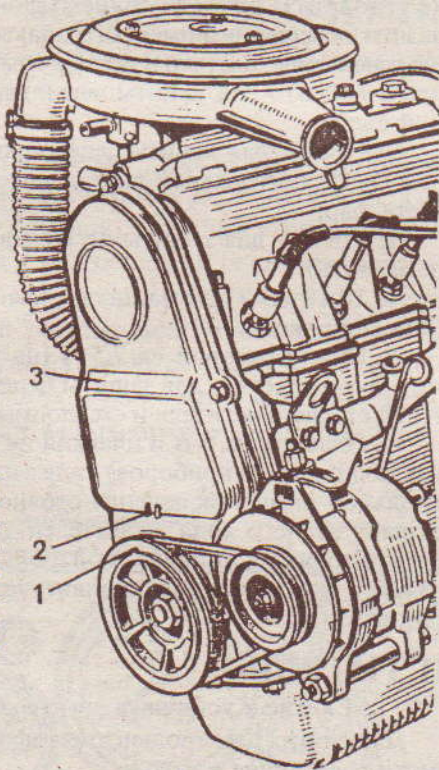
Метки установки момента зажигания: 1 - метка (выступ) на шкиве коленчатого вала; 2 - метка М3; 3 - наружный кожух плоскозубого ремня
